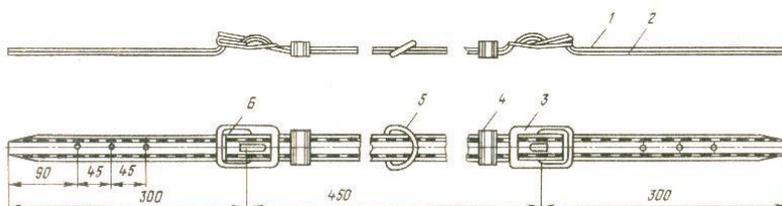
Нагрудник: 1 – ремень верхний; 2 – ремень подстрочный; 3 – антабка; 4 – шлевка; 5 – рамка; 6 – пряжка шпеньковая
